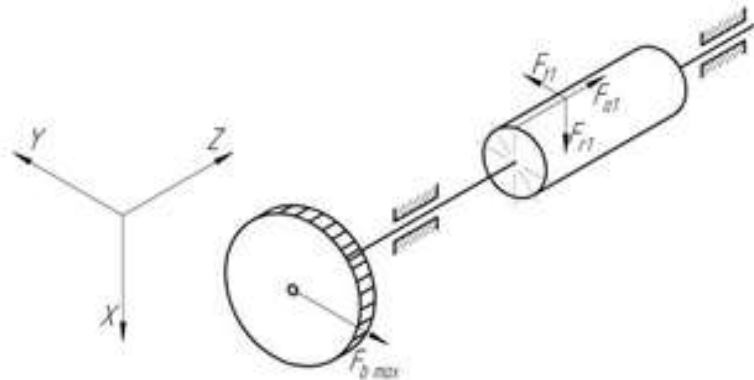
Силова схема швидкохідного вала черв'ячної передачі
